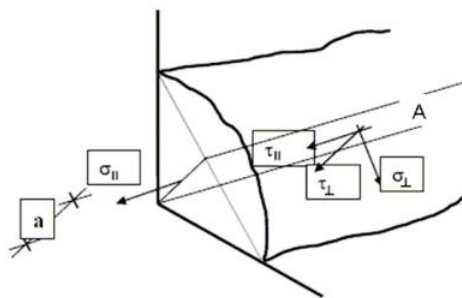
Distribución de las tensiones en un cordón de soldadura. Fuente: Catedra de Unión de Materiales por Soldadura.
